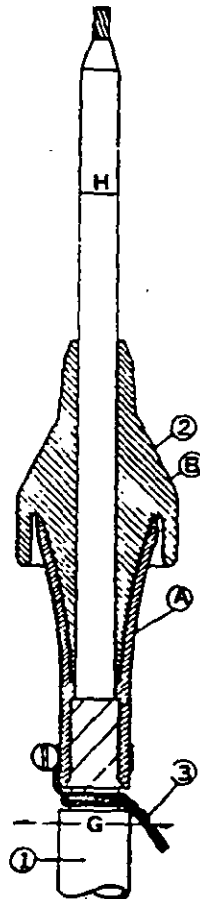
Detalle constructivo de la terminal para uso en interiores (TIP).
